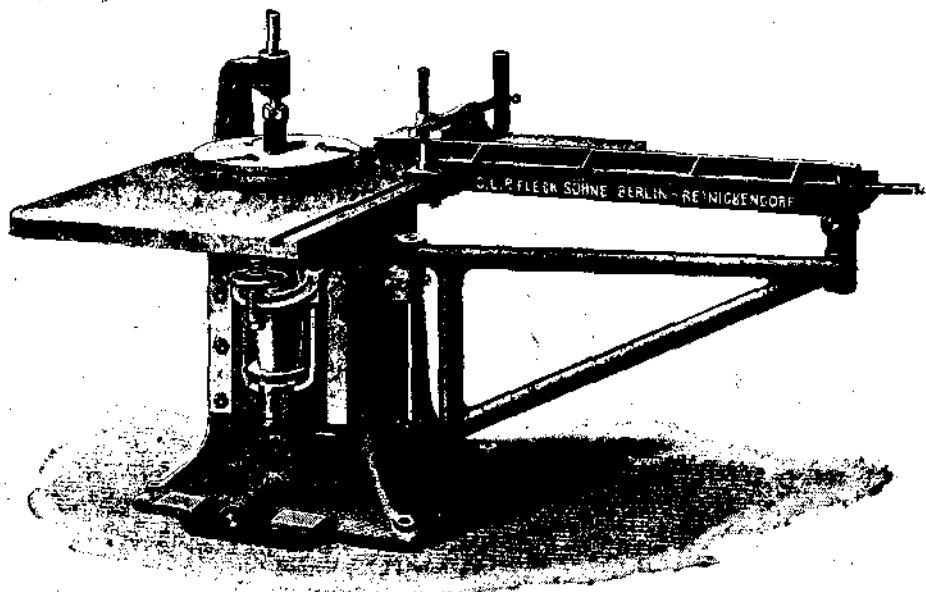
Тяжелый фрезерный станок с боковыми салазками.
